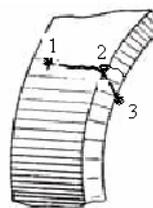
Схема заварки трещины на крыле автомобиля
